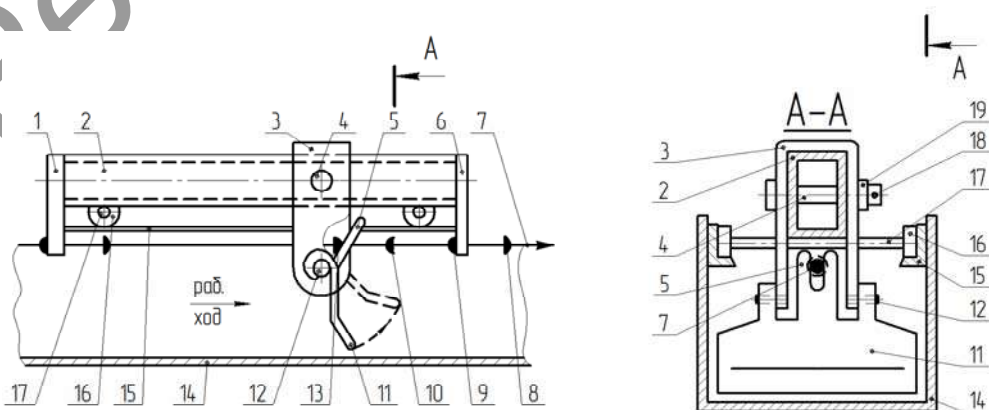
Фрагмент шагового транспортёра для перемещения заготовок
